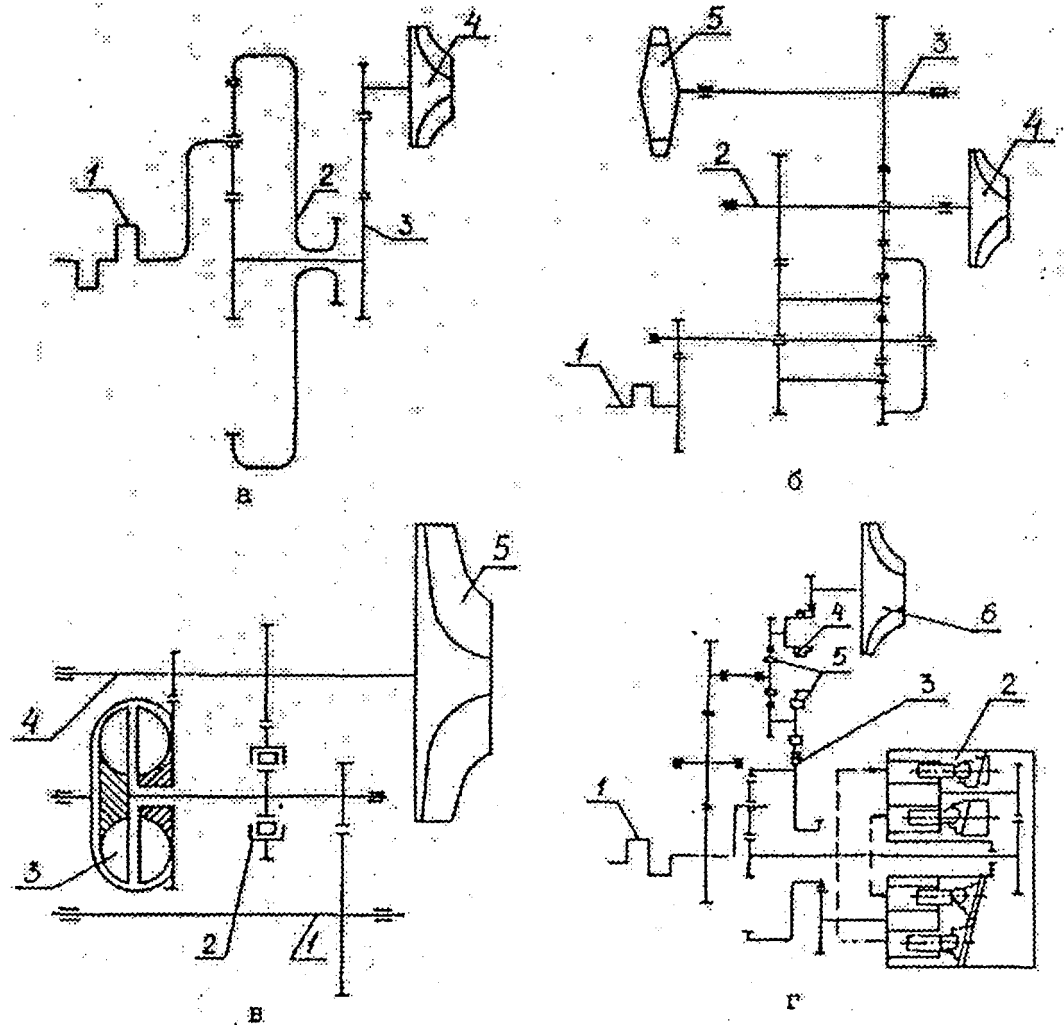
Схемы механической связи компрессора с коленчатым валом[2/];
